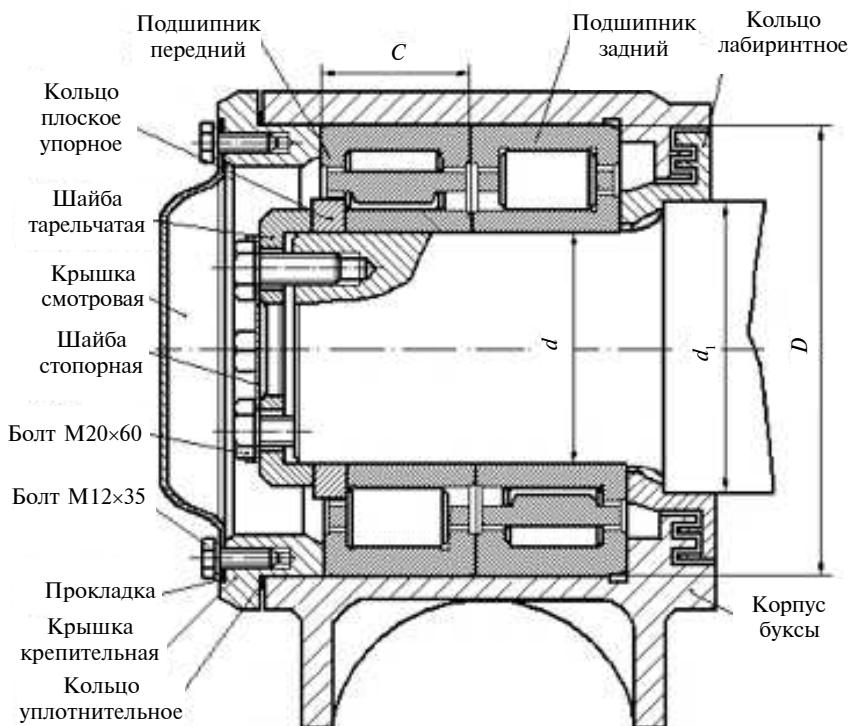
Буксовый узел с двумя подшипниками роликовыми цилиндрическими с торцевым креплением шайбой тарельчатой и болтами М20
